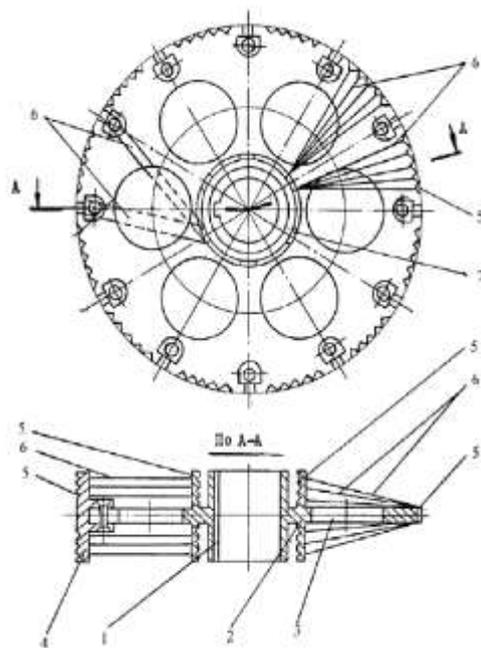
Общий вид колеса со струнными элементами центробежного насоса-мешалки и разрез А-А
